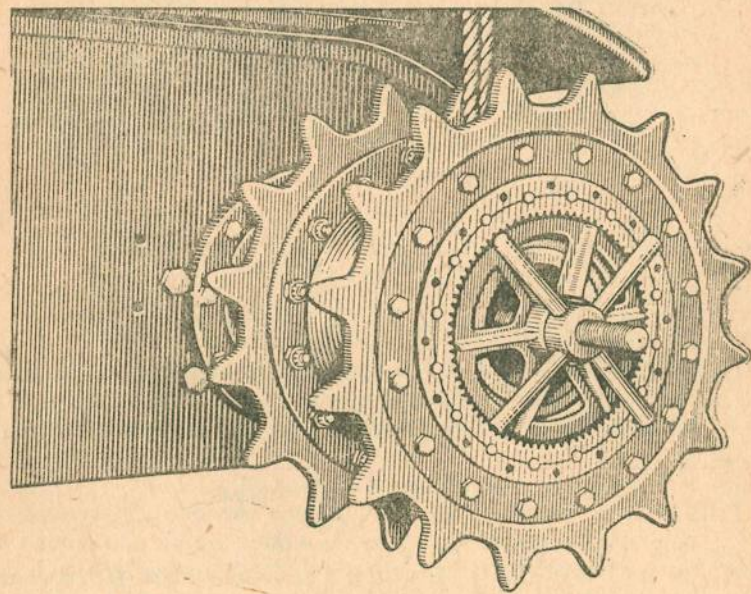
Запрессовка ведущего колеса на кронштейн при помощи приспособления № 5212
